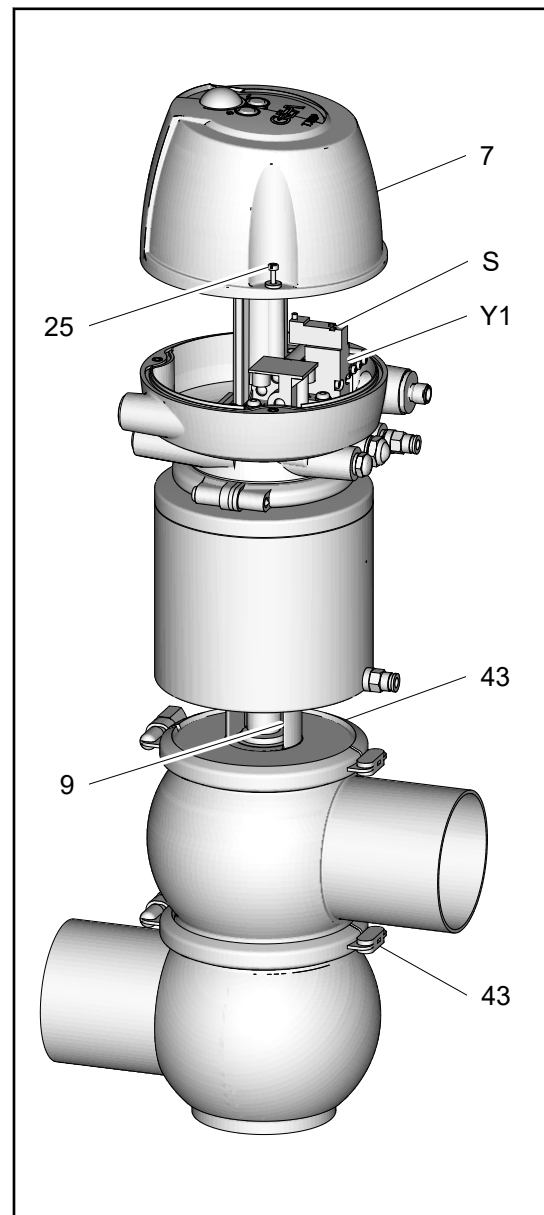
Ausführung mit 2 Gehäusen
